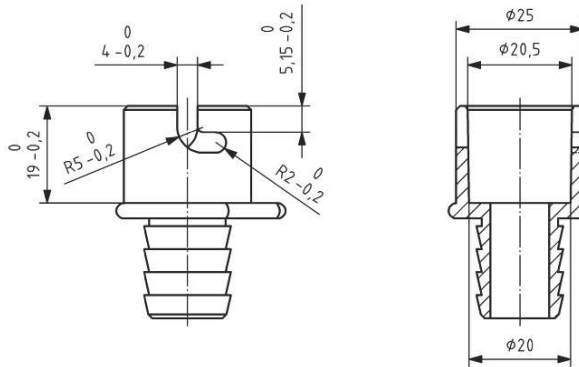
Anschlussvorrichtung mit typischen Maßen
